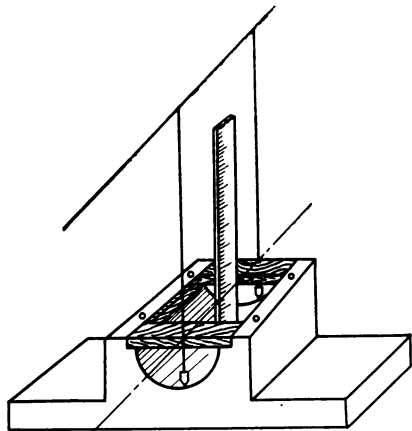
Контроль установки подшипников главного вала подъемной машины
